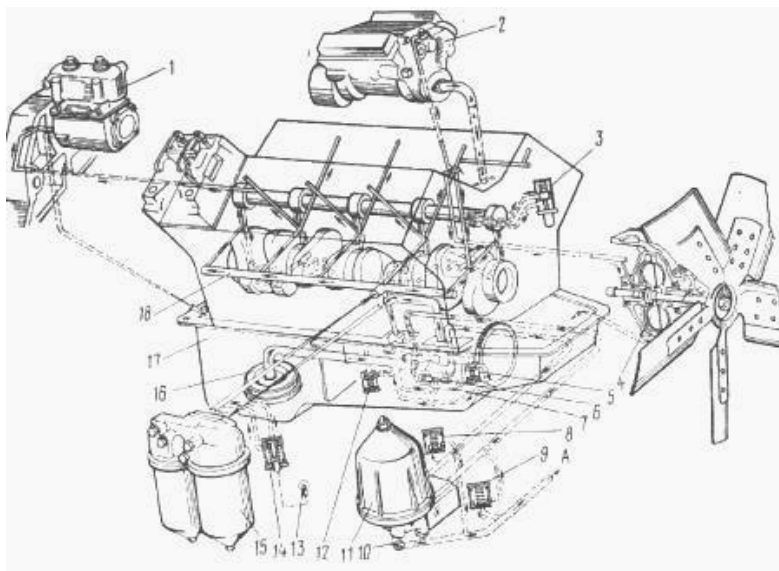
Система смазки двигателя КамАЗ-70
